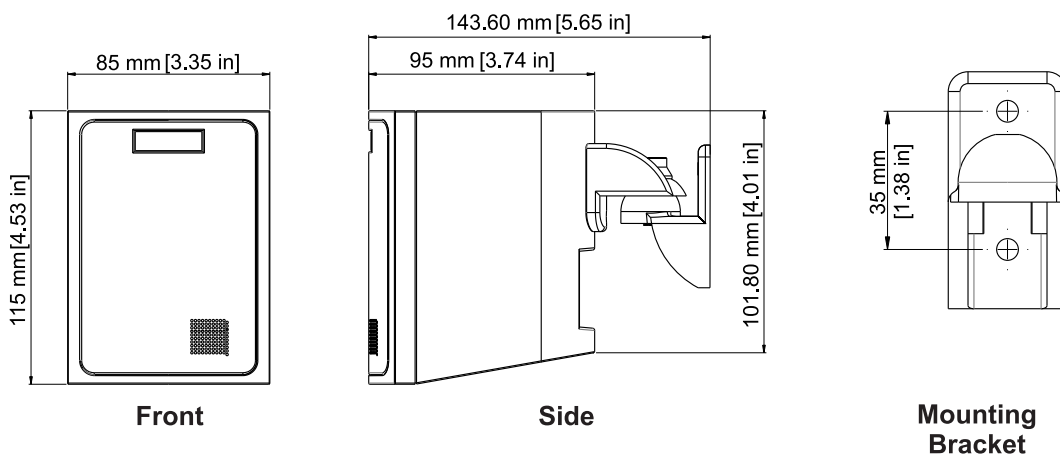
Dimensiones LB6-S-D y soporte de montaje
